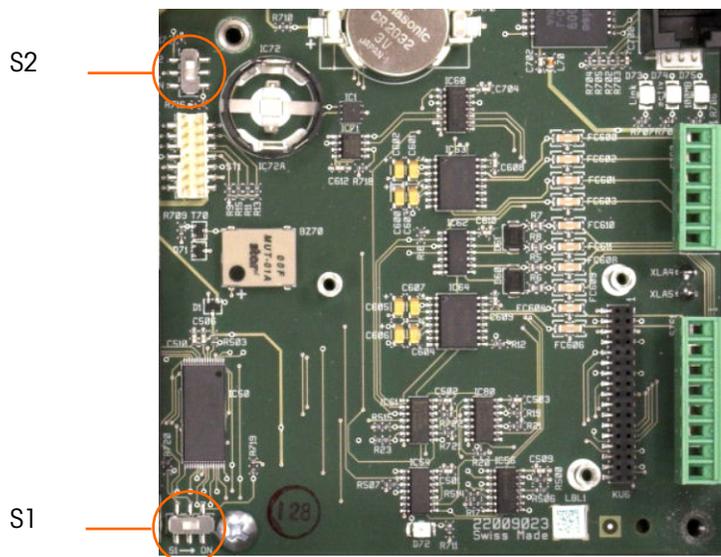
Emplacement des commutateurs de la carte PCB principale
